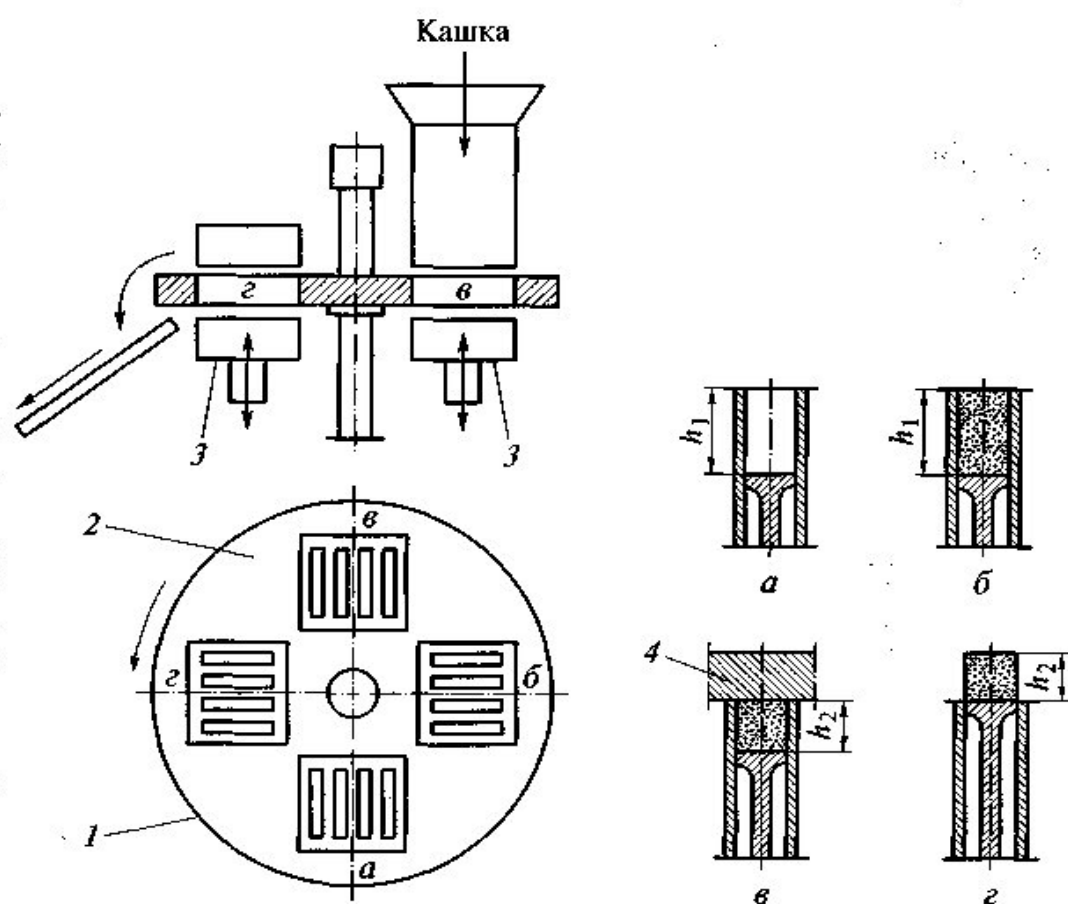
Карусельный пресс с возвратно-поступательным движением пуансона:
